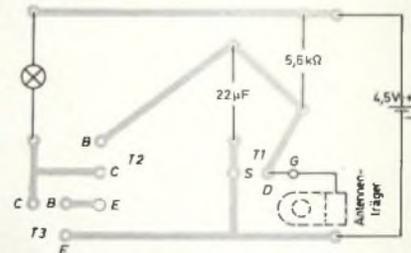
Bestückungsplan der Platine für die Schaltung im Bild 2
